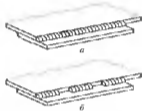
Непрерывный (а) и прерывистый (б) сварные швы
